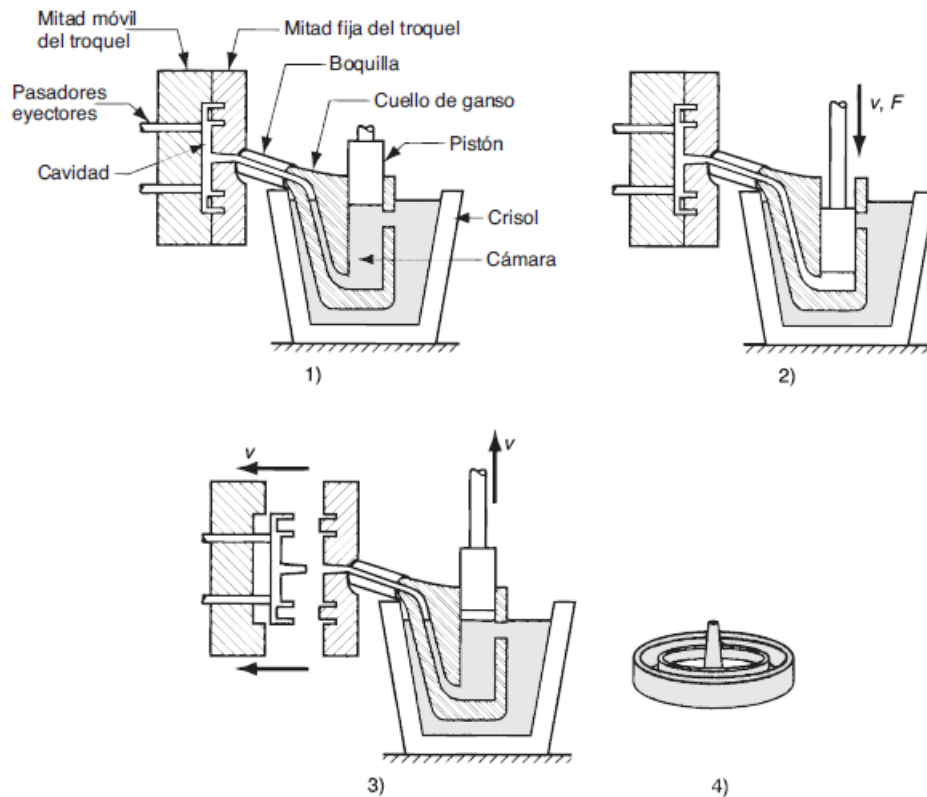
Moldeo en troquel en cámara caliente [2].
